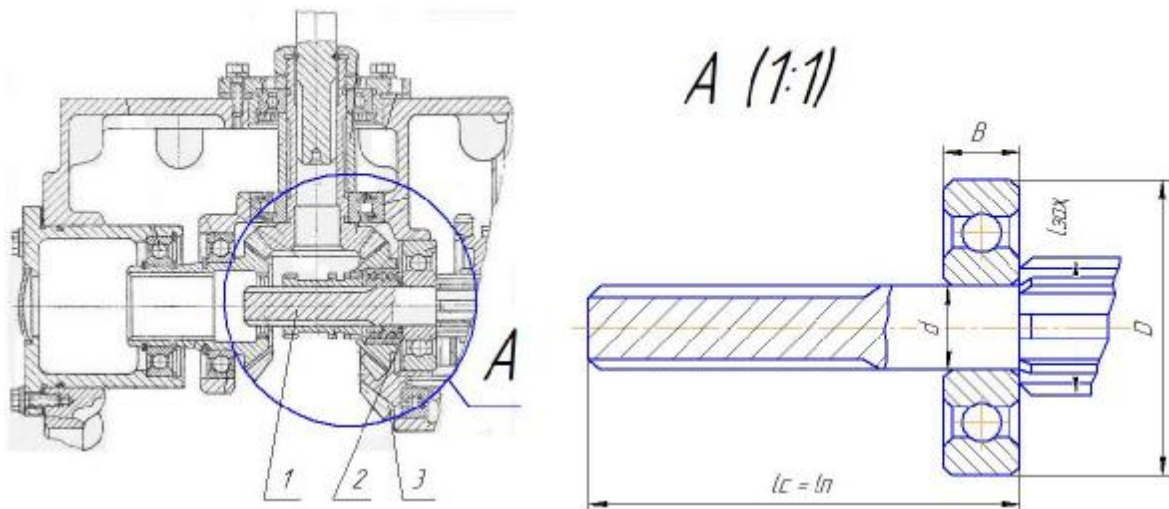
Схема встановлення кулькового підшипника на первинному валу коробки передач трактора Т-3512: 1 – первинний вал; 2 – підшипник первинного вала; 3 – вторинний вал.
